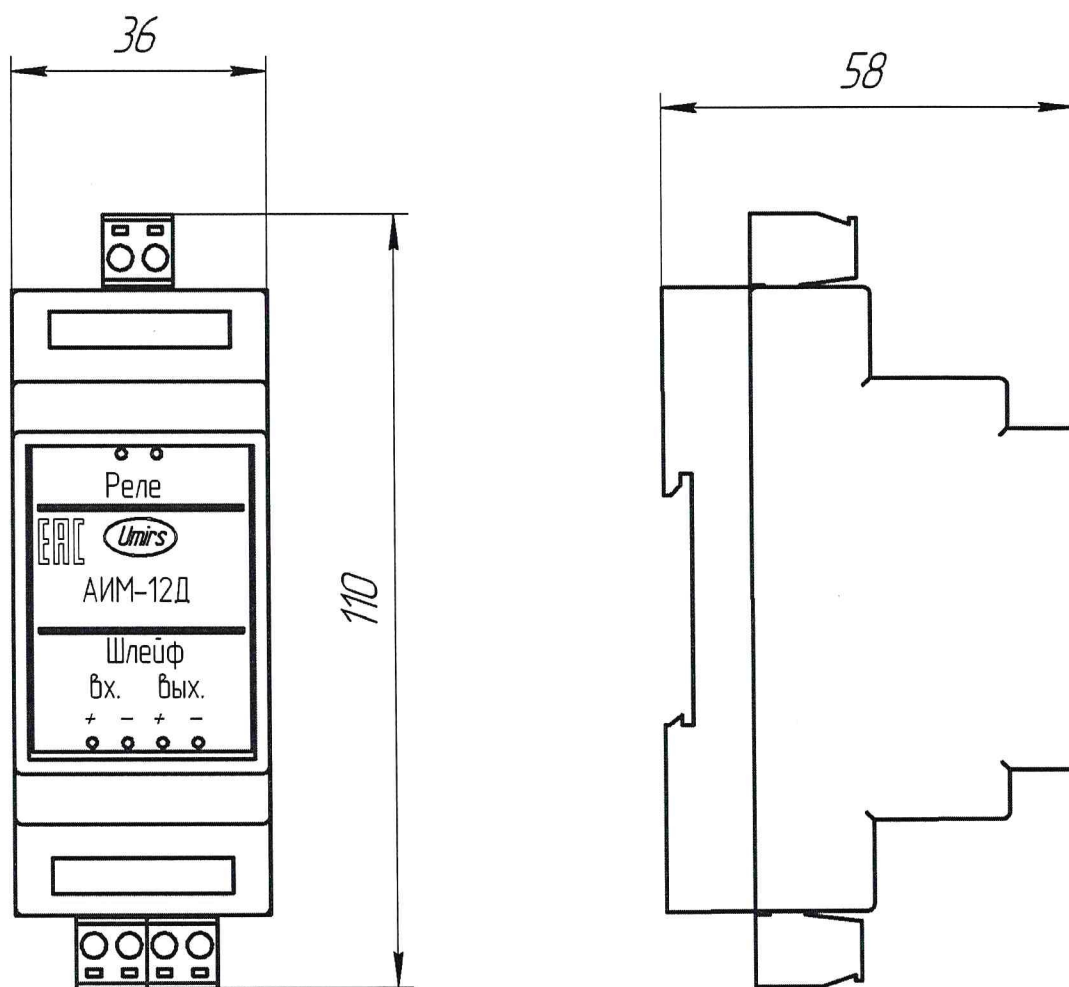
Габаритные и установочные размеры АИМ-12Д
